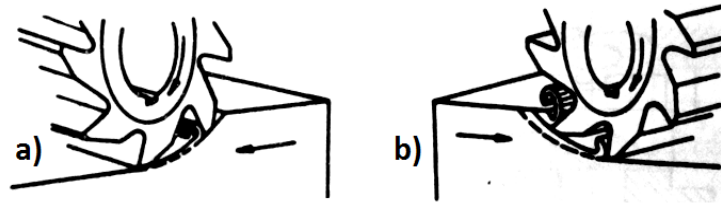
a) Fresagem concordante; b) Fresagem discordante; [Dino Ferraresi, 1990].
